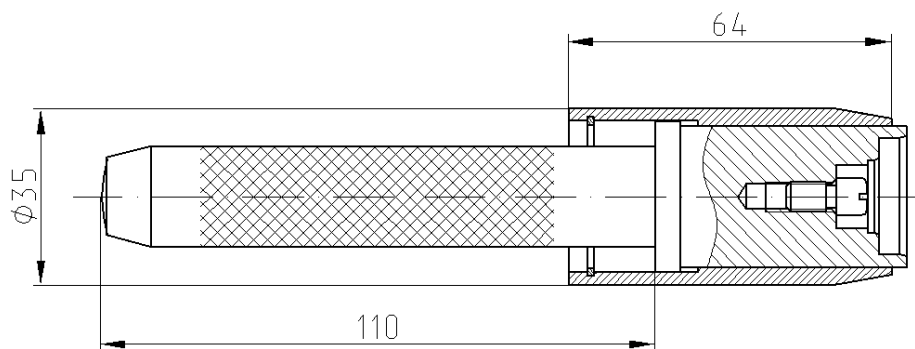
ЗМ 7853-4355 – Оправка для напрессовки
